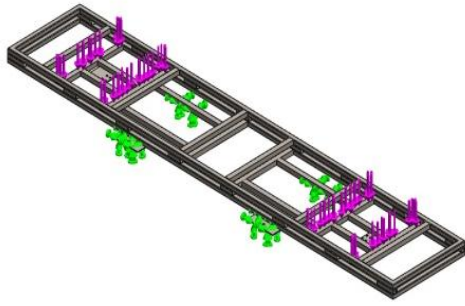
Cargas que se aplican a la plataforma de elevación
